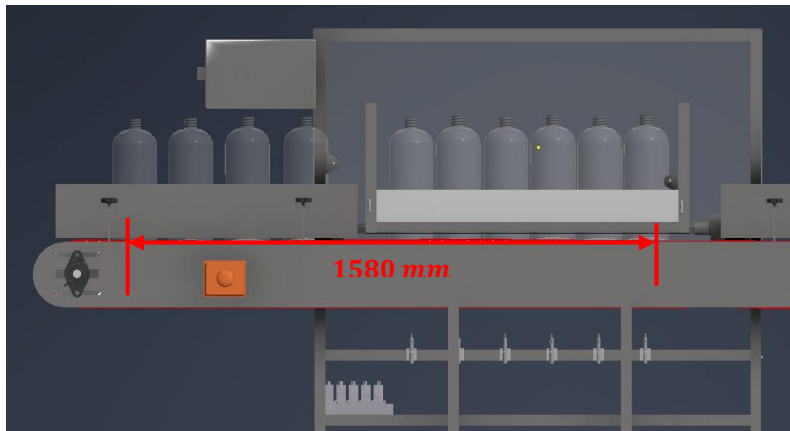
Distancia de recorrido para la entrada y cámara de lavado.
